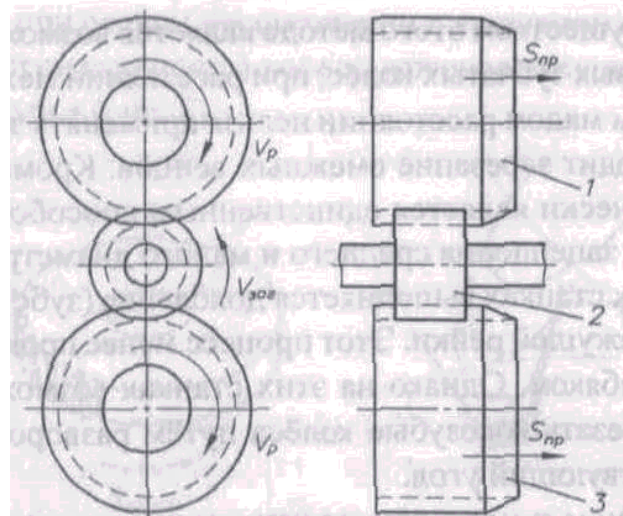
Схема накатывания зубчатого венца: 1, 3 – накатные ролики; 2 – накатываемое колесо
